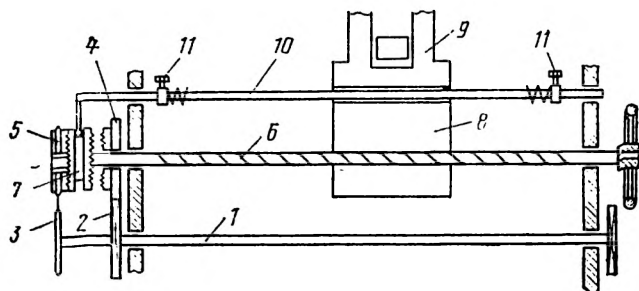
Схема механизма раскладки с червяком односторонней нарезки и зубчато-цепным приводом.
